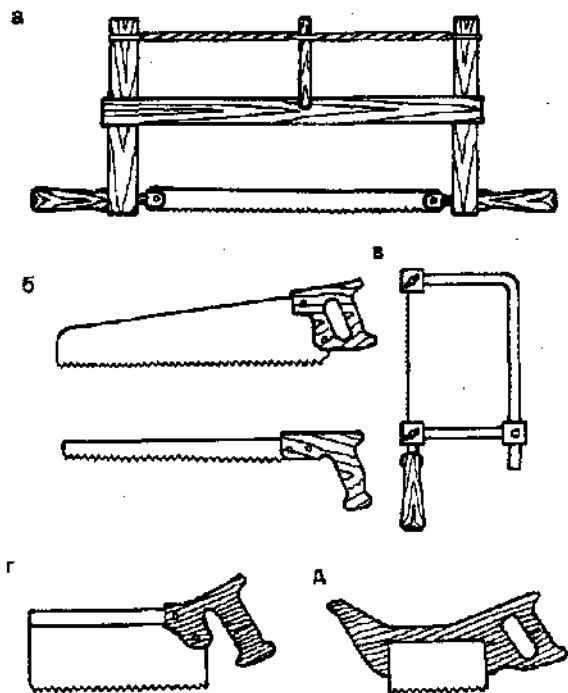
, Пилы: а — лучковая; б — ножовки; в — лобзик; г — обушковая пила; д — наградка
